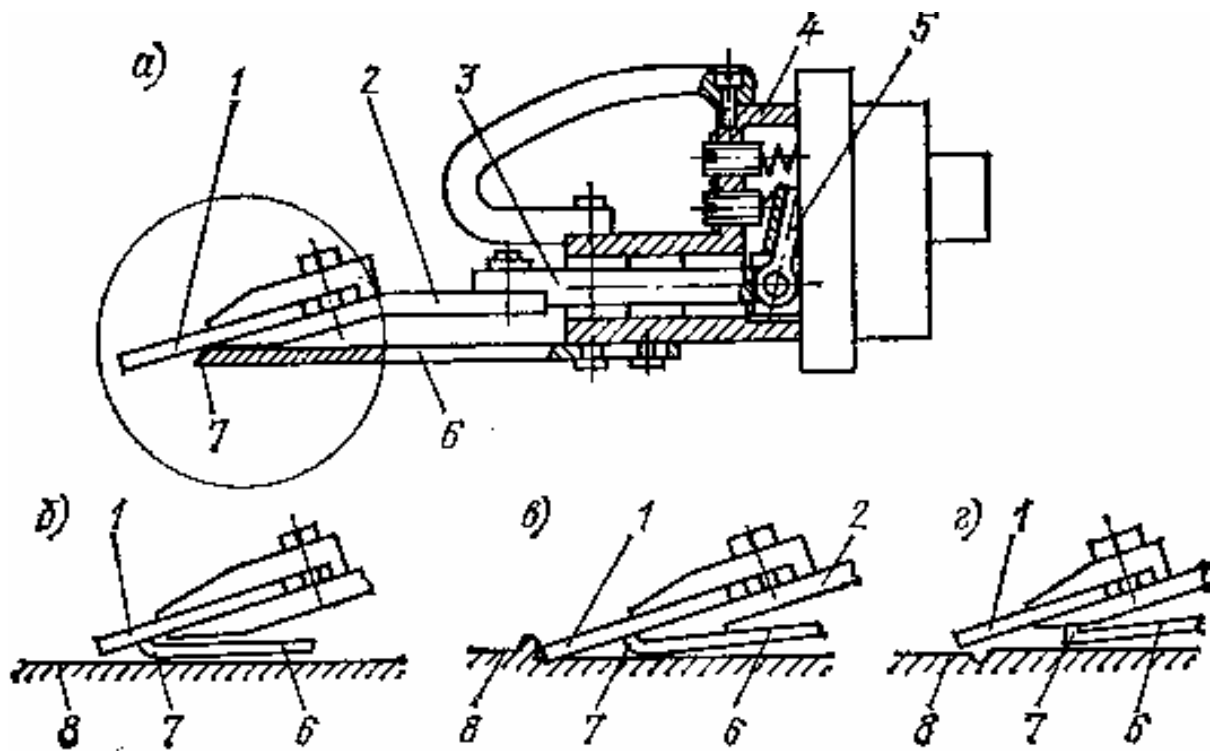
Конструктивна схема та схема роботи та схеми роботи механічного шабера
